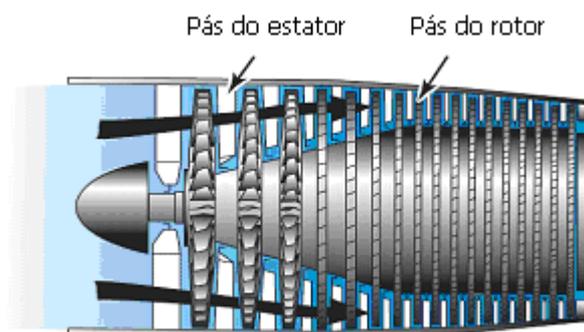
Pormenor da passagem convergente entre o estator e rotor
